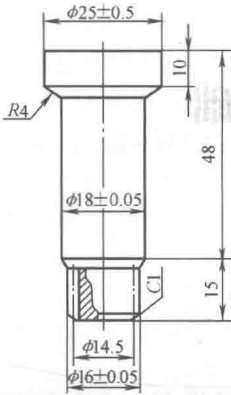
冷挤压中碳钢洗衣机齿轮轴
